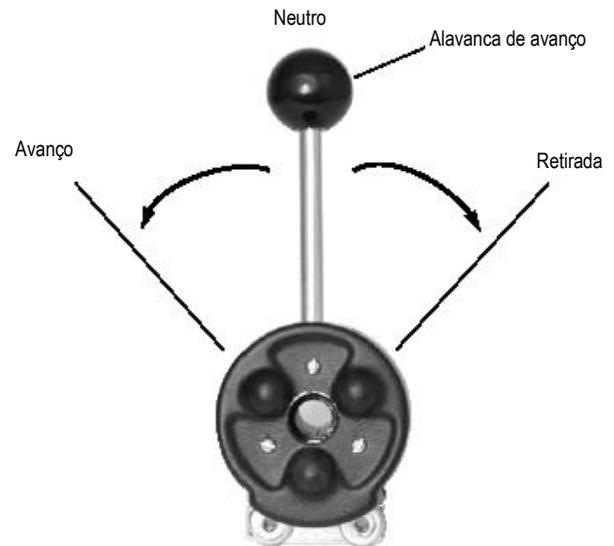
Sentidos de movimento do AUTOFEED (vista frontal da máquina)
